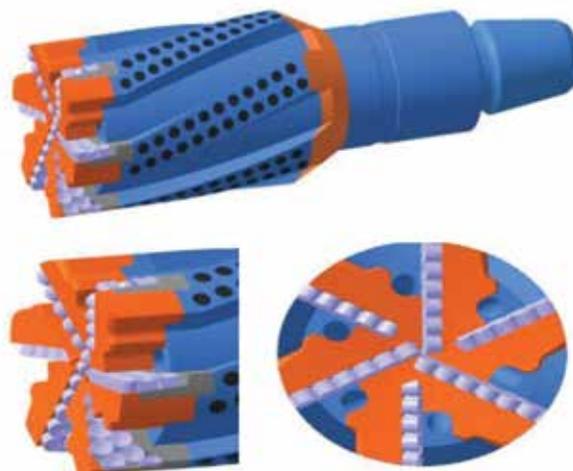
Фрезер для фрезерования композитных пакер-пробок
